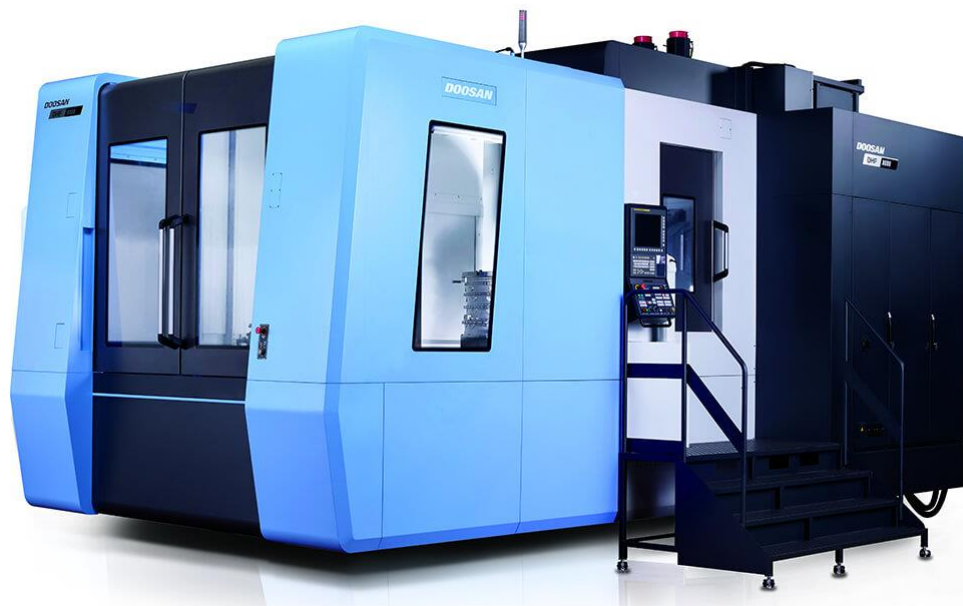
5-осевой горизонтальный центр DHF 8000 с высокой жесткостью конструкции станка
